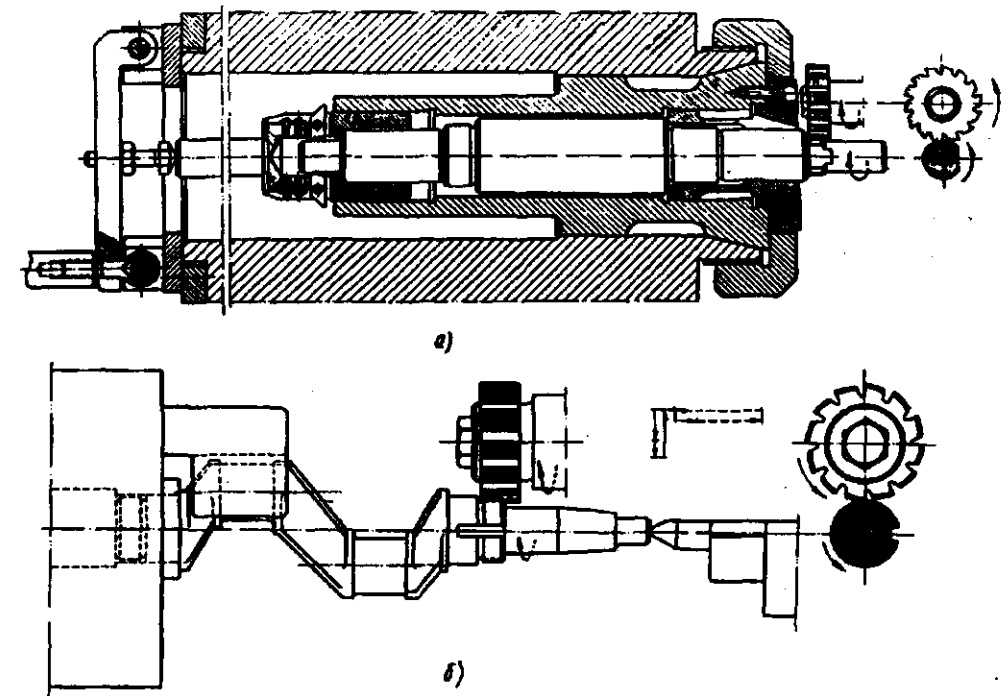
Настройки резьбофрезерного станка: а – с установкой заготовки через шпиндель; б – для фрезерования резьбы на коленчатом валике
